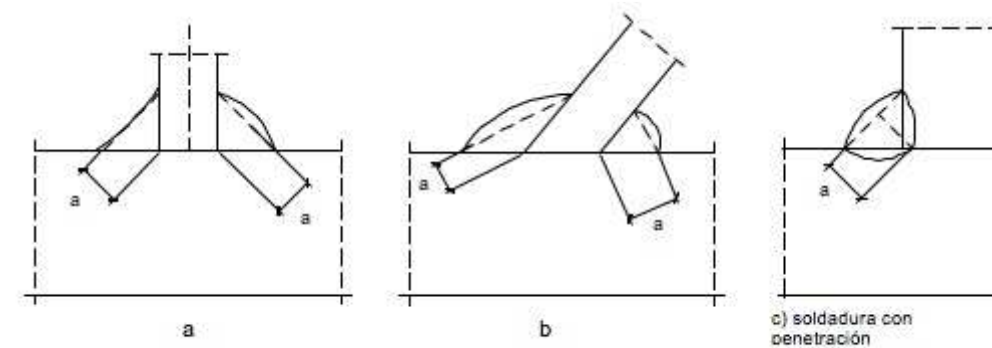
Soldadura en ángulo. Espesor de garganta
